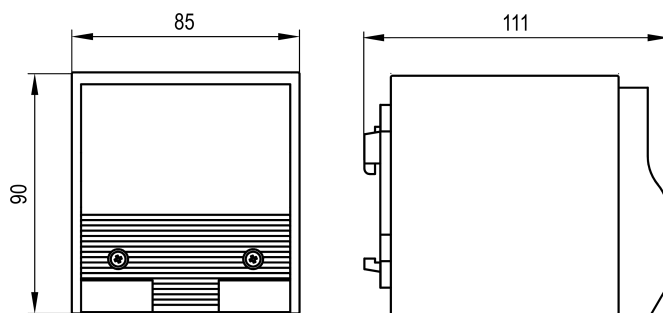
Габаритные размеры МТК-ЕFххх
